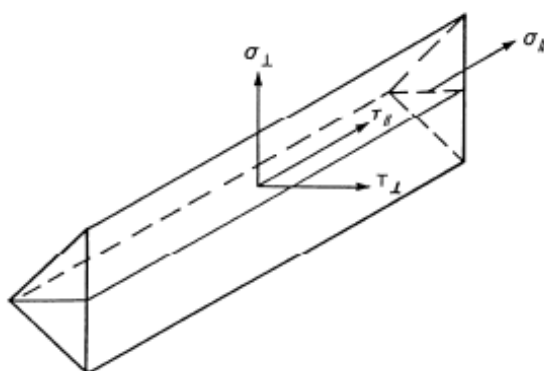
Componentes das tensões num cordão de soldadura
